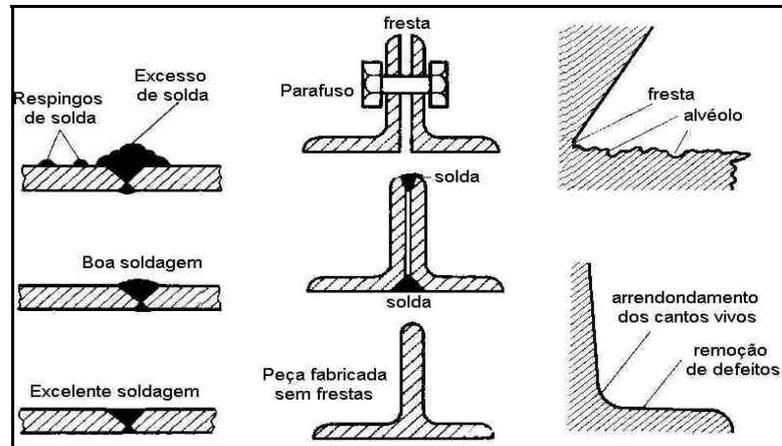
Elementos construtivos existentes na construção e montagem de equipamentos.
